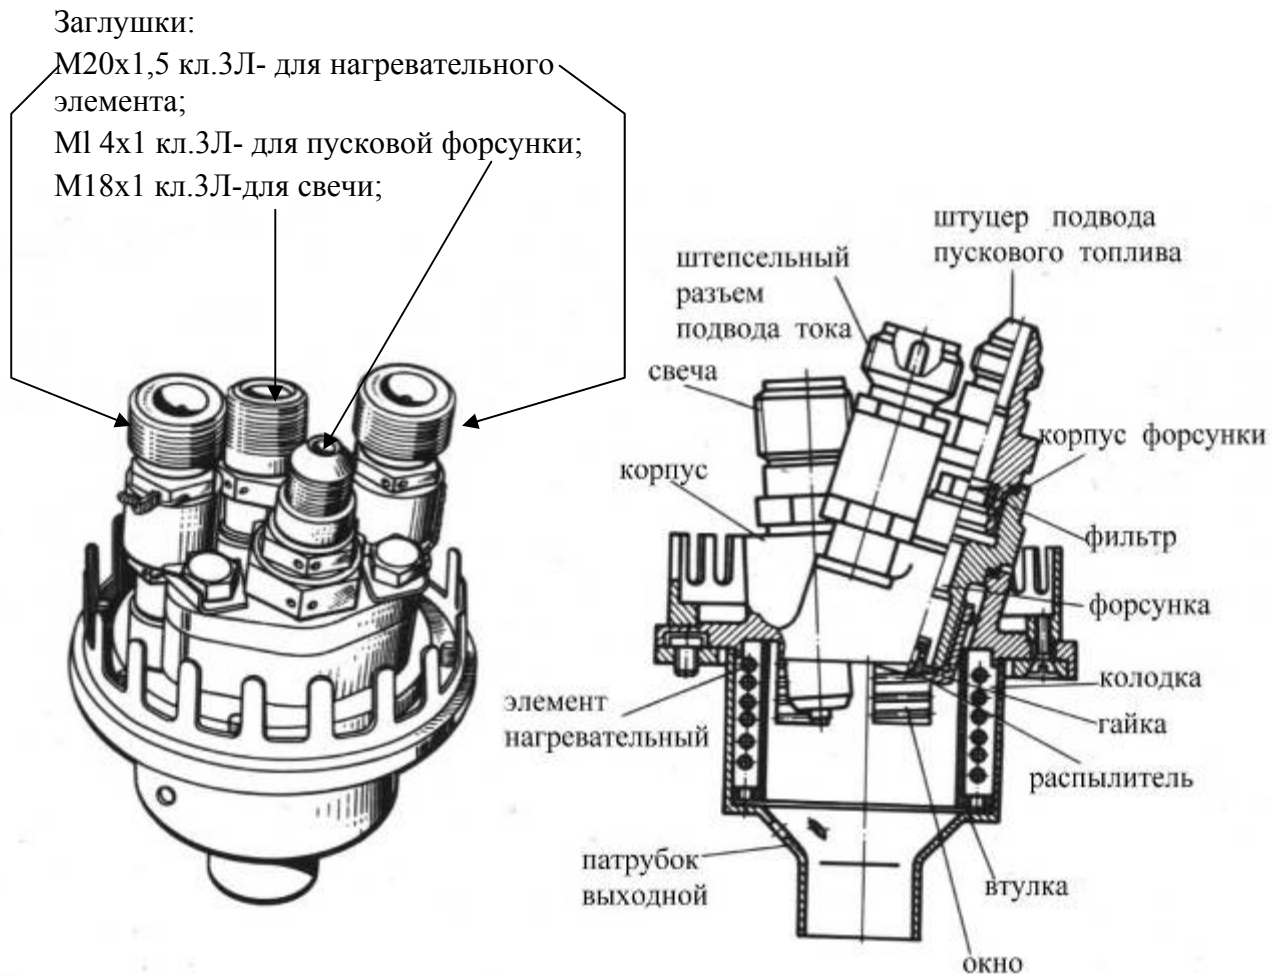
Общий вид и детали воспламенителя двигателя НК-86
